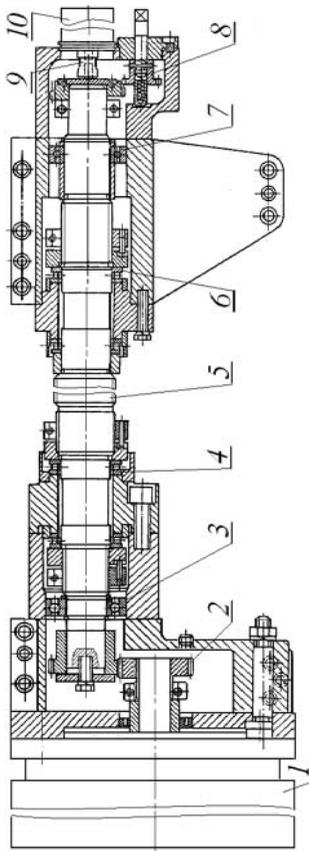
Привод продольной подачи салазок суппорта токарного станка с ЧПУ модели 16K20Ф3
